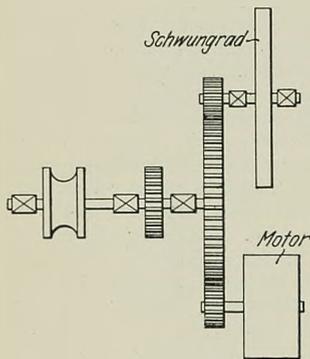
Schema des Schweißrollenantriebes.
